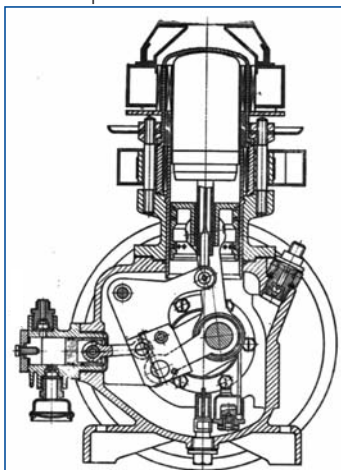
Разрез двигателя Стирлинга фирмы "Филипп"
